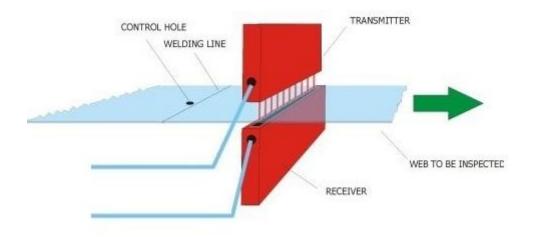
Схема работы детектора сварного шва: Control hole (контрольное отверстие); Welding line (сварочная линия); Receiver (приемник); Transmitter (передатчик); Web to be inspected (проверенная (осмотренная) полоса)
